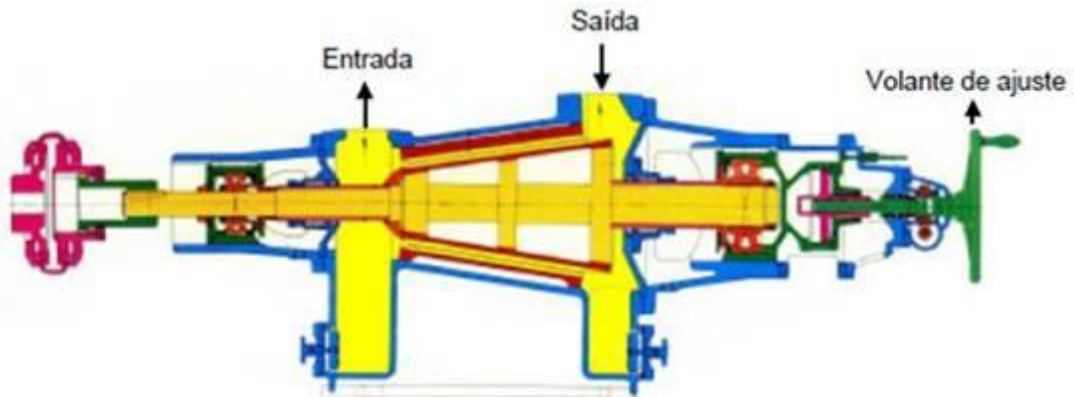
(FONTE: Fabricação de Papel – Preparação de Massa (SENAI CETCEP))
